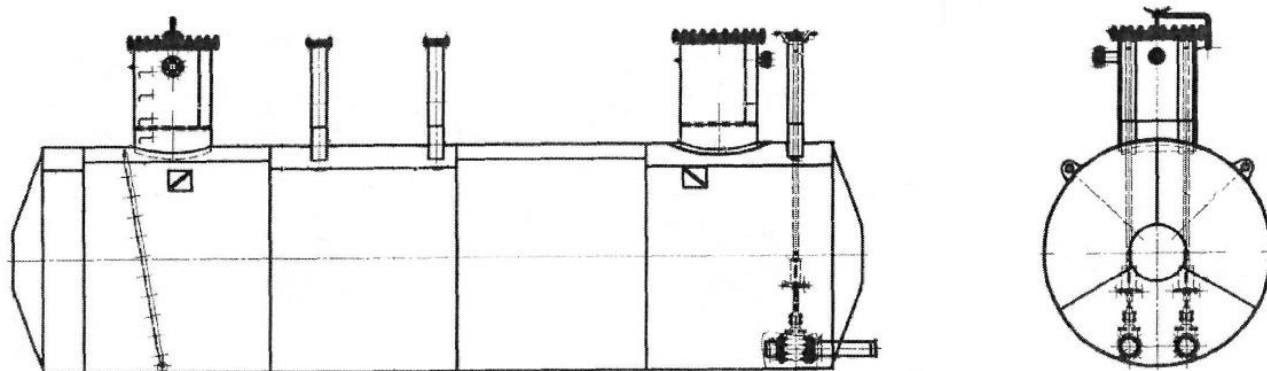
Эскиз общего вида резервуаров РГС-40
